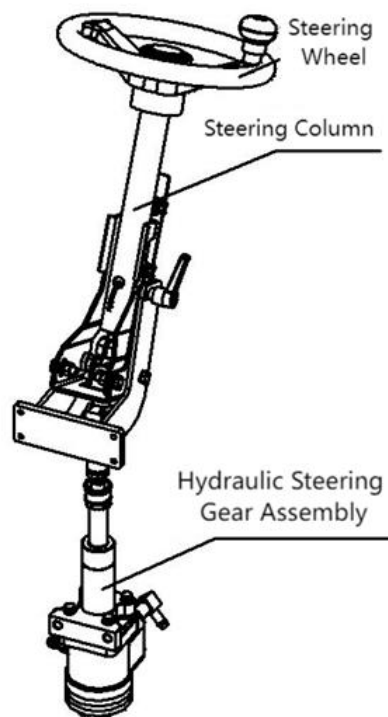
Схема конструкции рулевого управления вилочного погрузчика:
